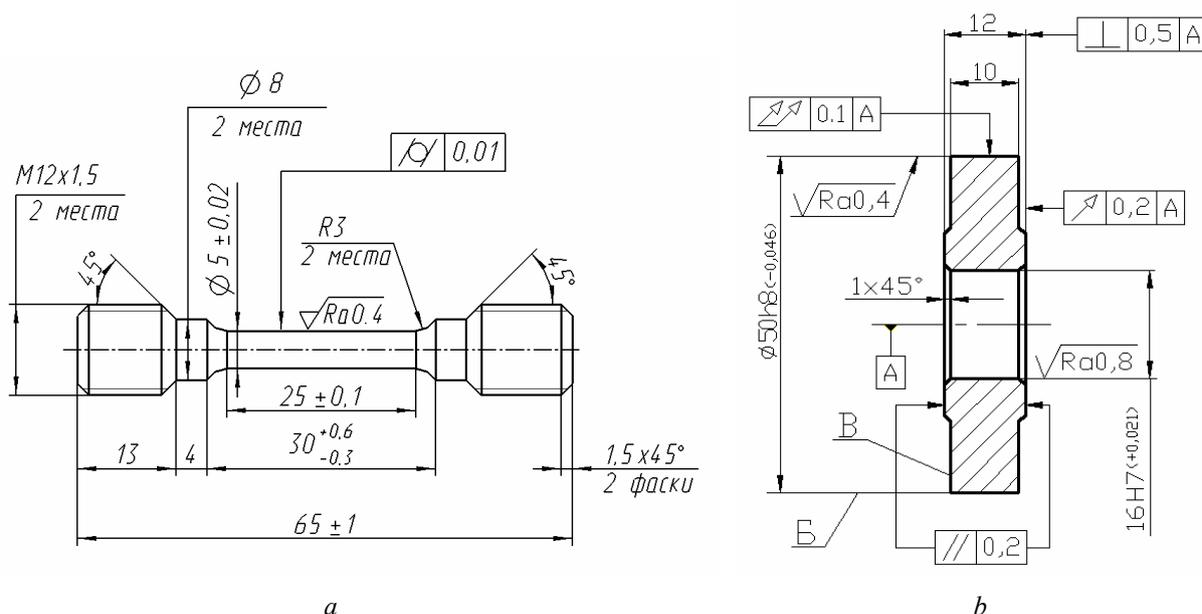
Эскизы опытных образцов: а – для растяжения; б – для обкатки
